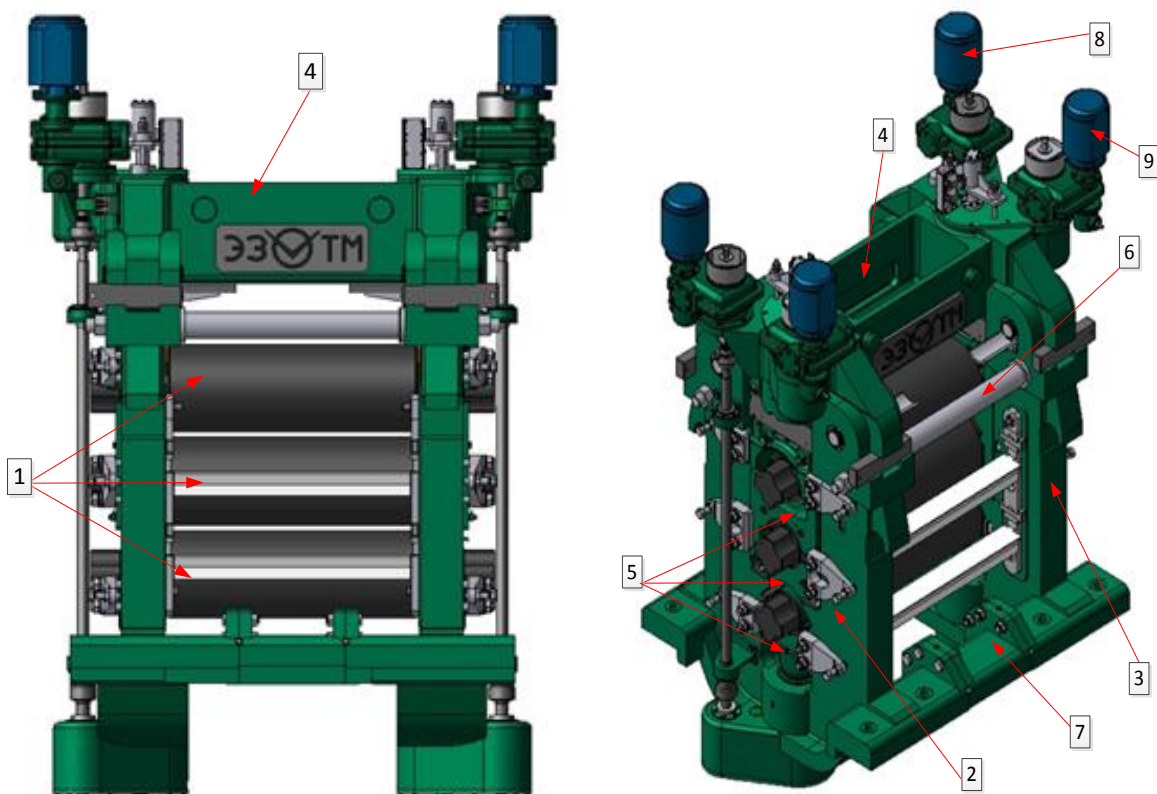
Конструктивная 3D-модель трехвалковой клетки:
